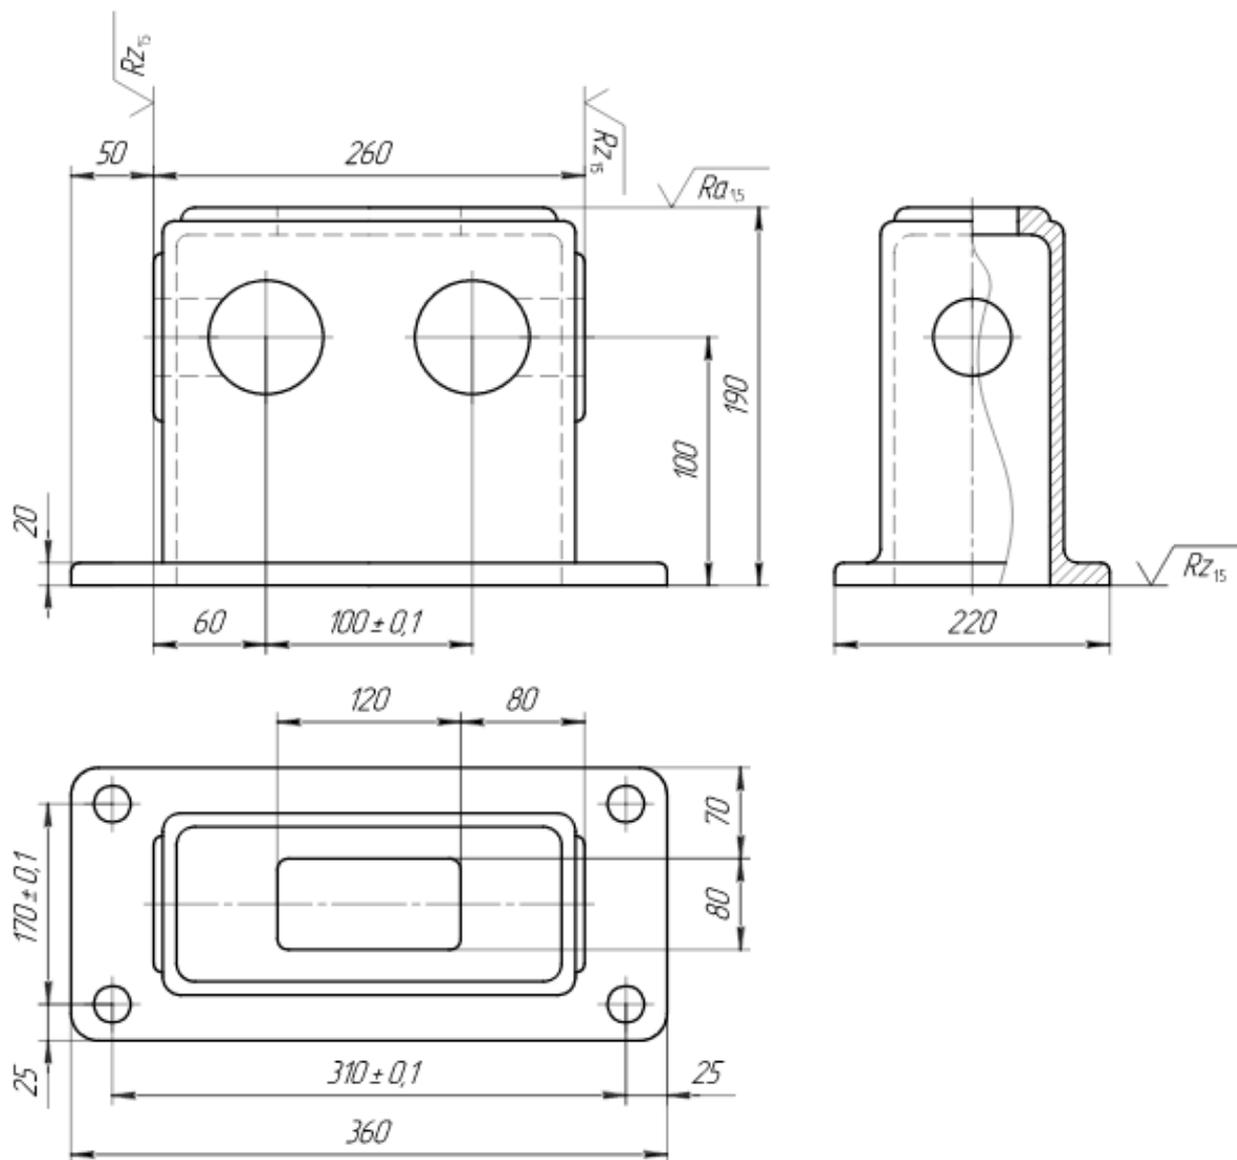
Эскиз корпусной детали к задаче 3.9
